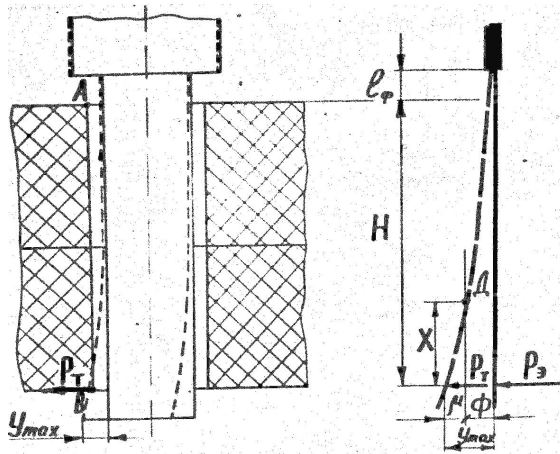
Схема контакта задней поверхности фрезы с обрабатываемым материалом
